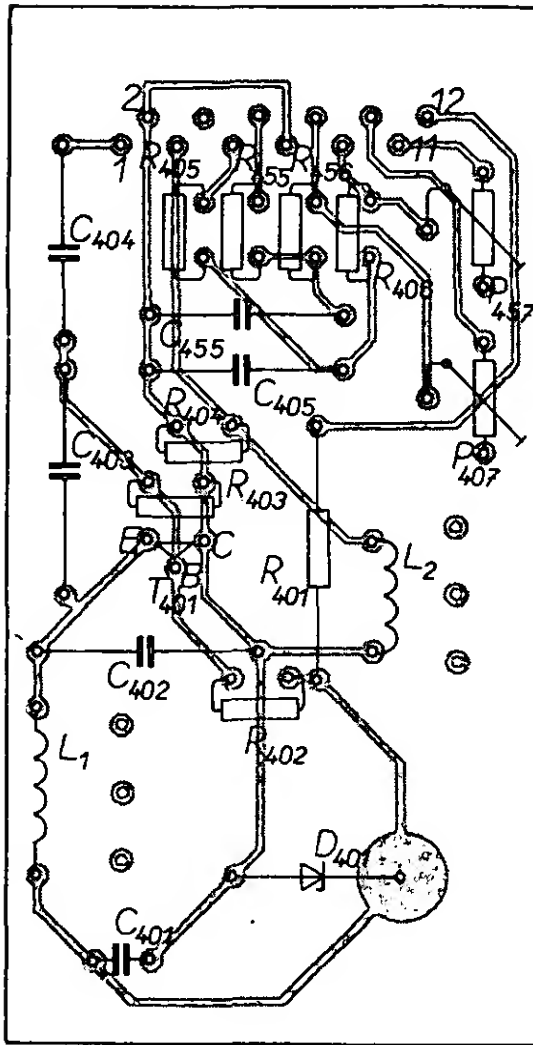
Deska s plošnými spoji oscilátoru (N27)
